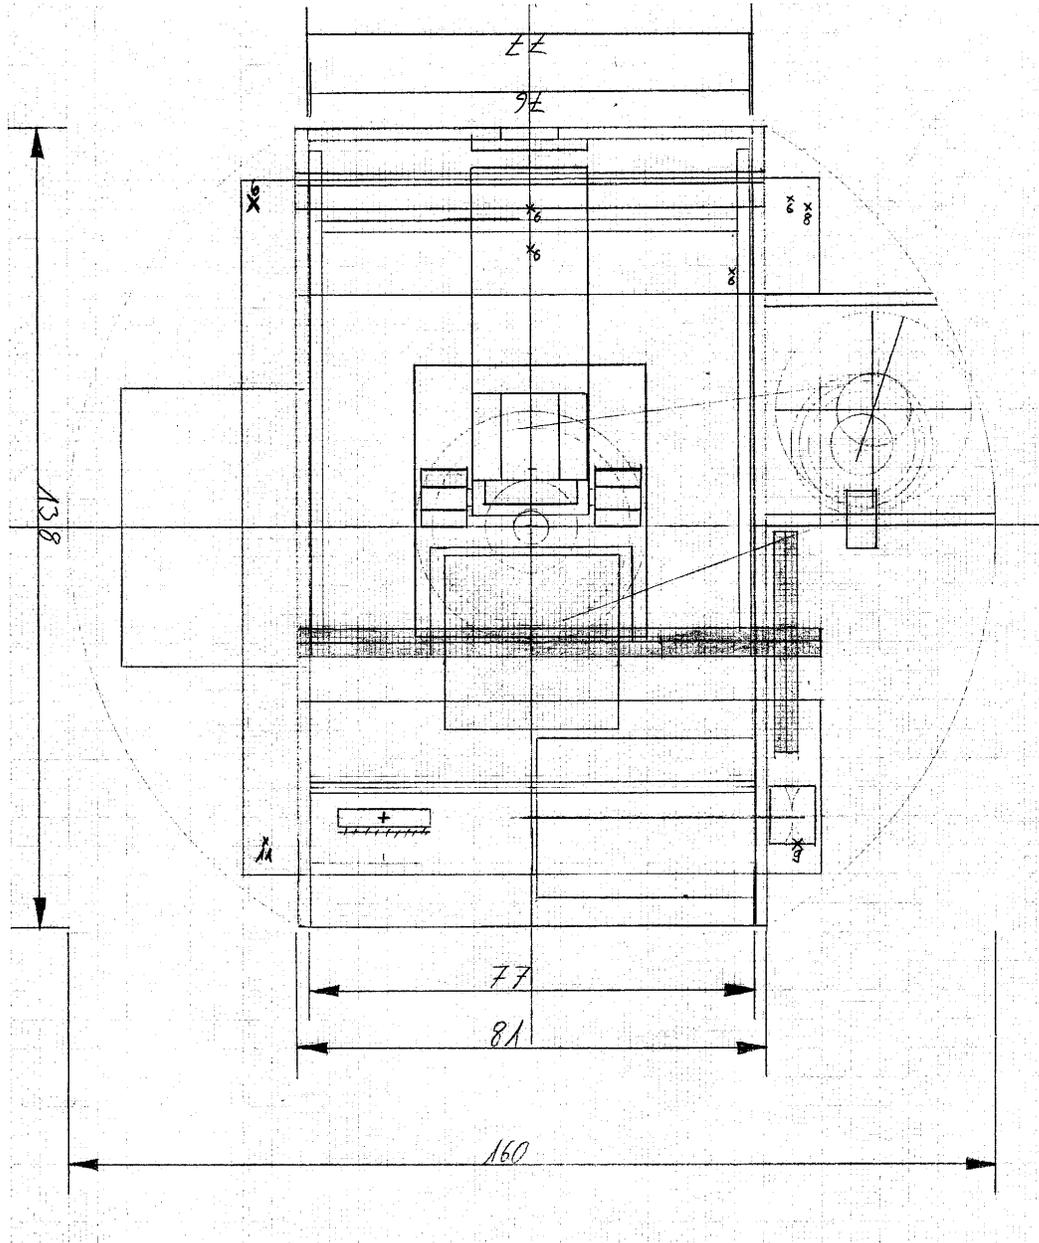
Zeichnung Draufsicht Kartenausteiler
